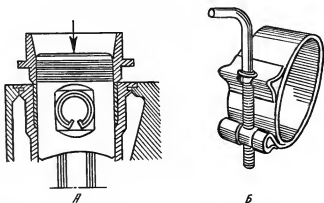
Приспособления для установки поршня с кольцами в цилиндр: а) оправка (в форме стального конусного кольца); б) ленточное.
